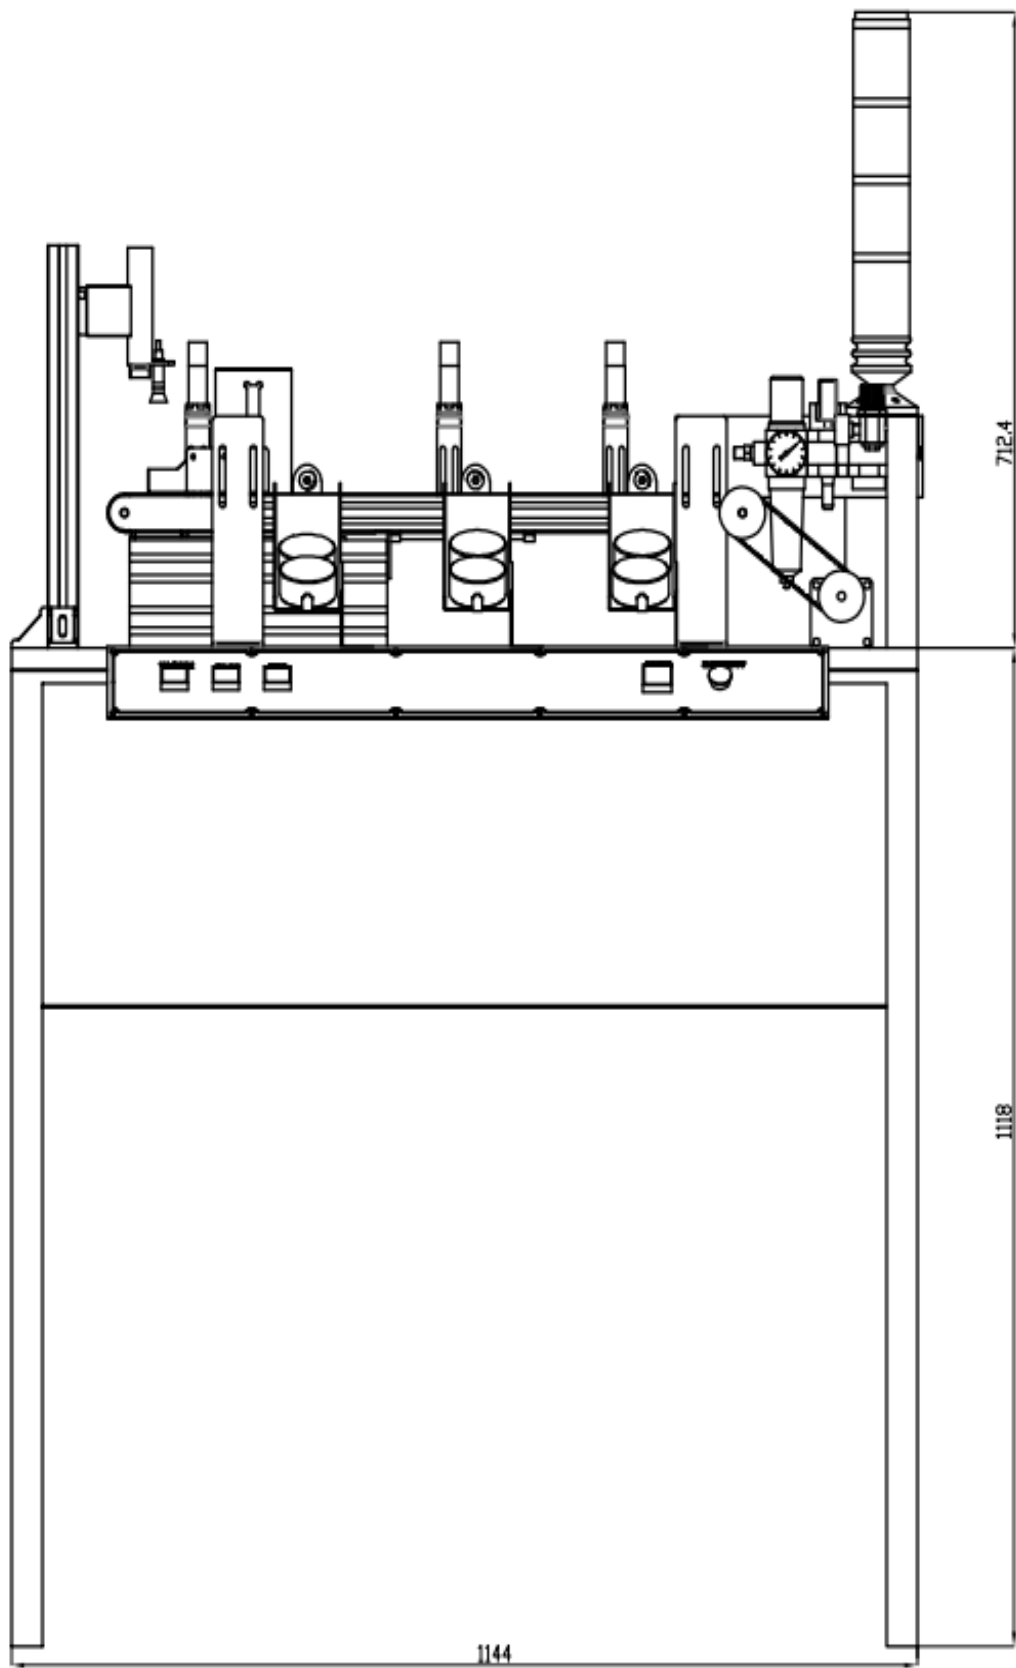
Hình chiếu đứng mô hình 3D hệ thống
